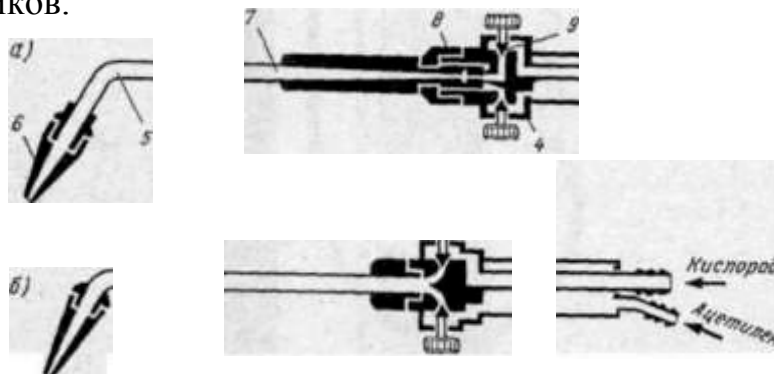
Типичная горелка для газовой сварки (а) и (б)
